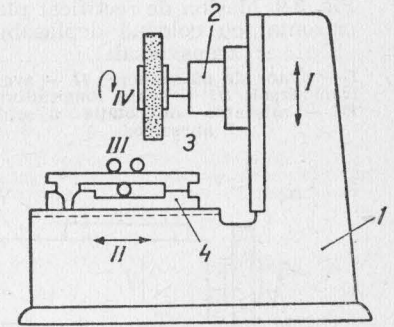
Mașină de rectificat plan orizontal cu masa deplasabilă transversal:
